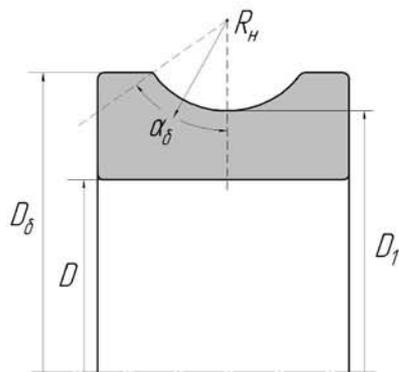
Основные размеры внутреннего кольца шарикового подшипника
